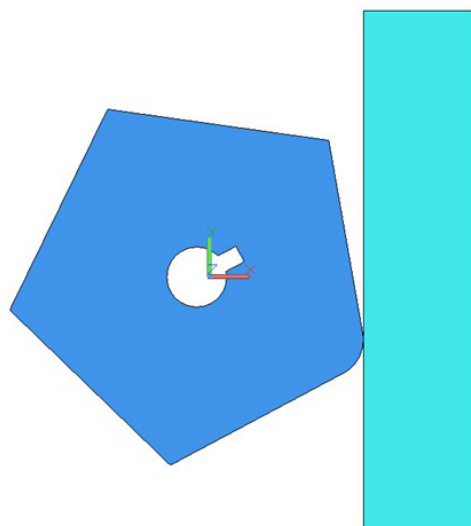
2D-модель формообразования многогранной твердосплавной пластины инструментом по второй кинематической схеме
